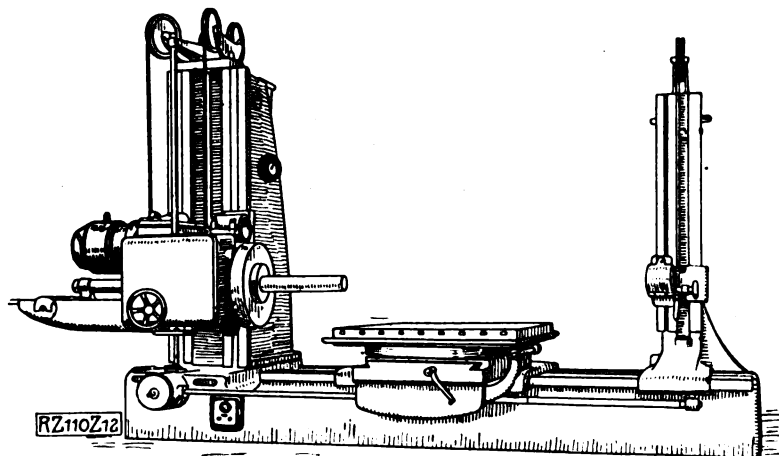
Wagerechthohrmaschine mit Motor am Spindelstock.
